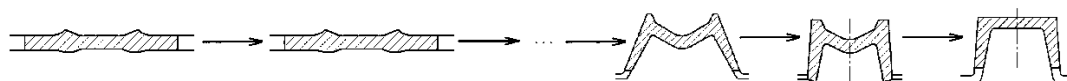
Схема калибровки прокатных валков по способу сгибания
